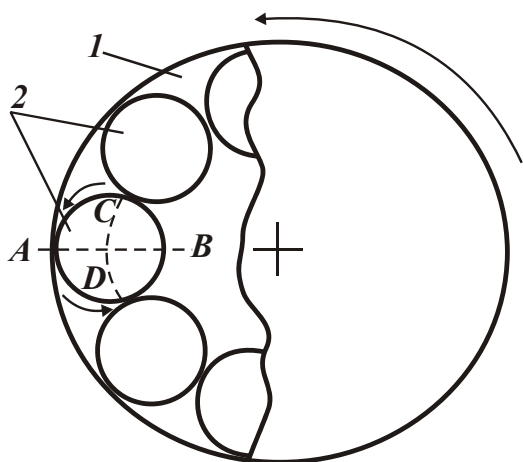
Схема шлифования чашечными или тарельчатыми кругами: 1 – вращающийся несущий диск; 2 – чашечные или тарельчатые круги.
